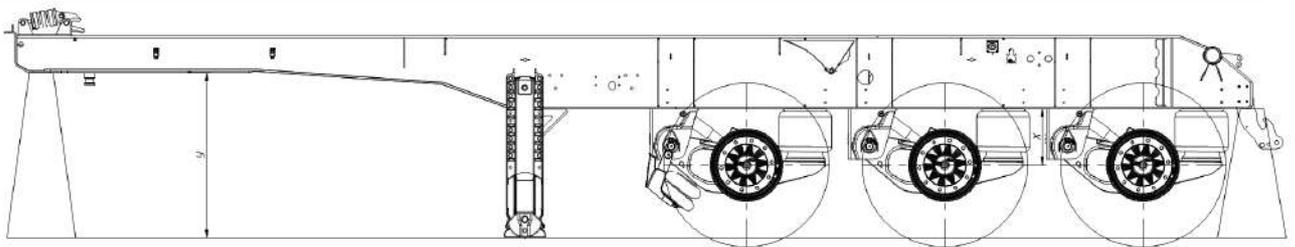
Схема установки полуприцепа для проверки движения по колее. Вид сбоку.
